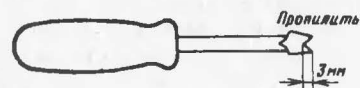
Приспособление для замены кинескопа в телевизоре "Шилялис-405Д-1"
